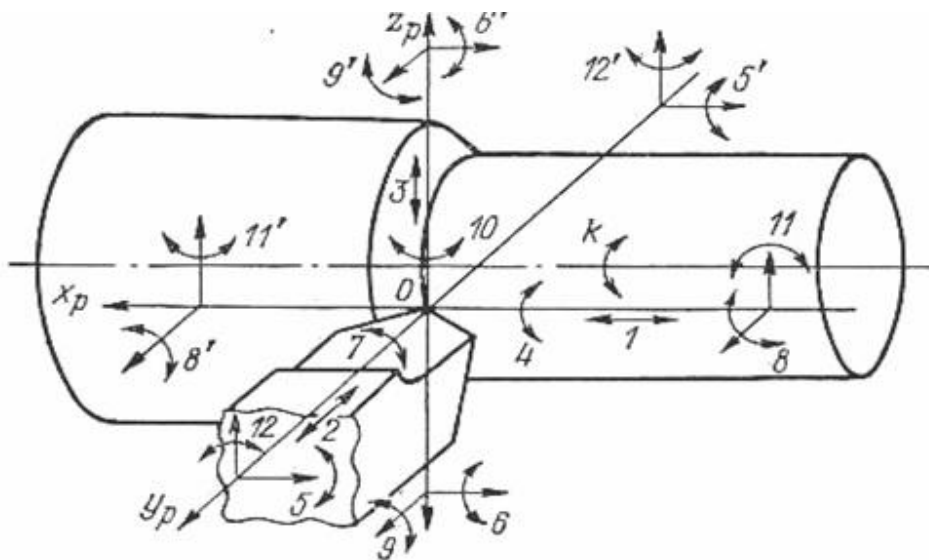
Схема напрямків відносних коливань інструменту і заготовки при точінні
